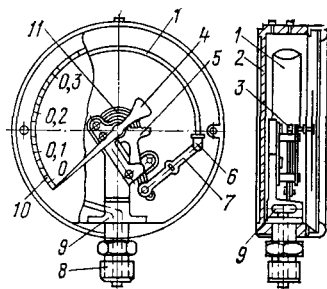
Пружинный манометр: 1 — трубчатая пружина; 2 — корпус; 3 — шестерня; 4 — стрелка; 5 — зубчатый сектор; 6 — пробка с шарнирной осью; 7 — поводок; 8 — штуцер; 9 — держатель; 10 — шкала; 11 — спиральная пружинка.
